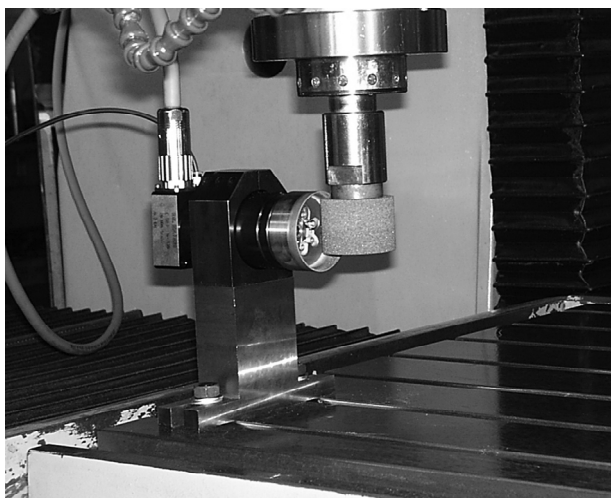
Установка шпинделя правящего круга на рабочем столе станка.
